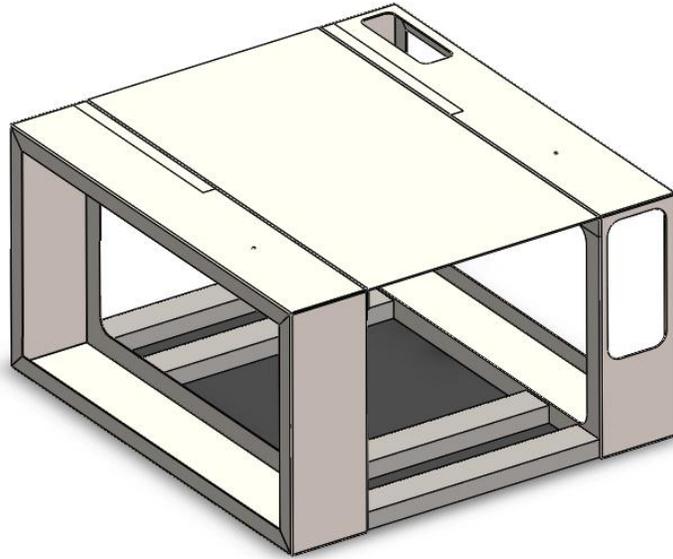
Châssis de la machine mouleuse rotative à biscuit
